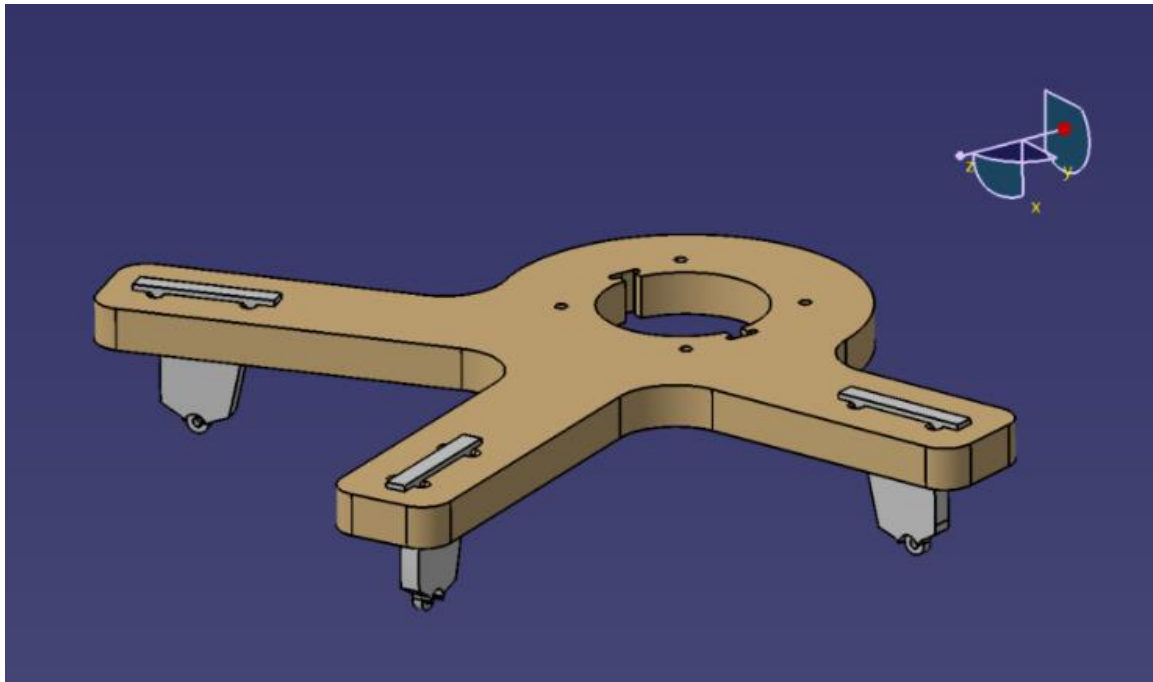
Positionierungsplatte mit Gegenstück der Hauptverbinder.
